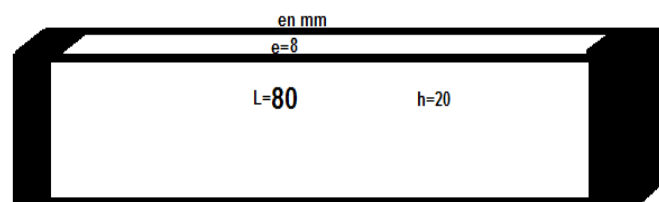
Dimensionnement de l'éprouvette, l=80mm, s=160mm²
